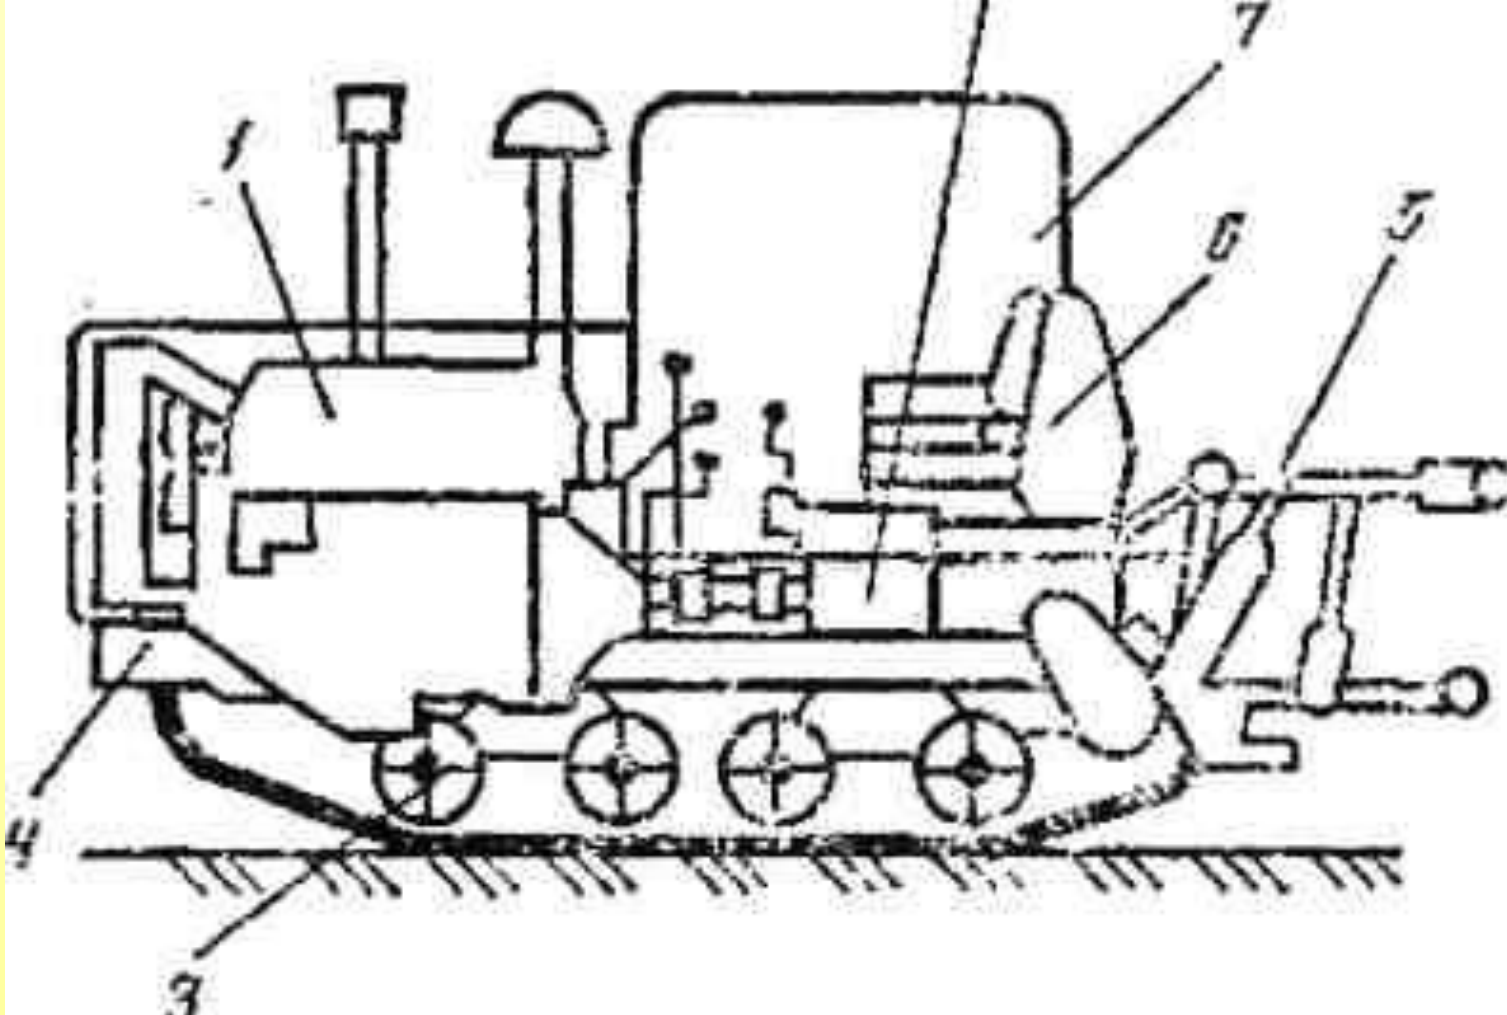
Общий вид гусеничного трактора ДТ-75МВ:
